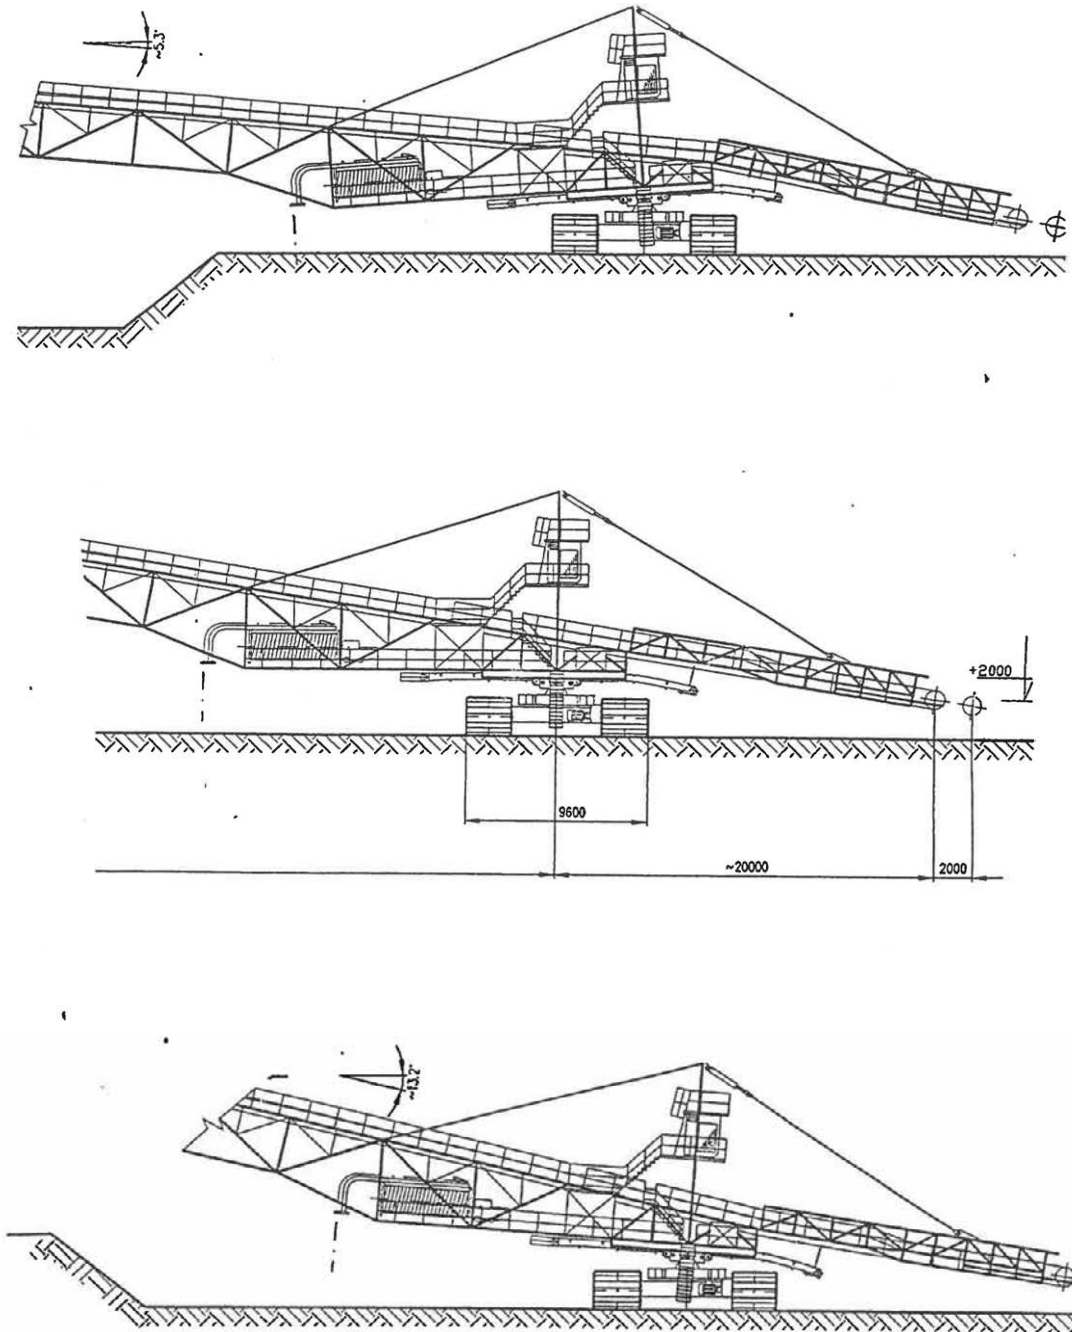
Řešení středního přesypu zakladače ZPDH 6300
